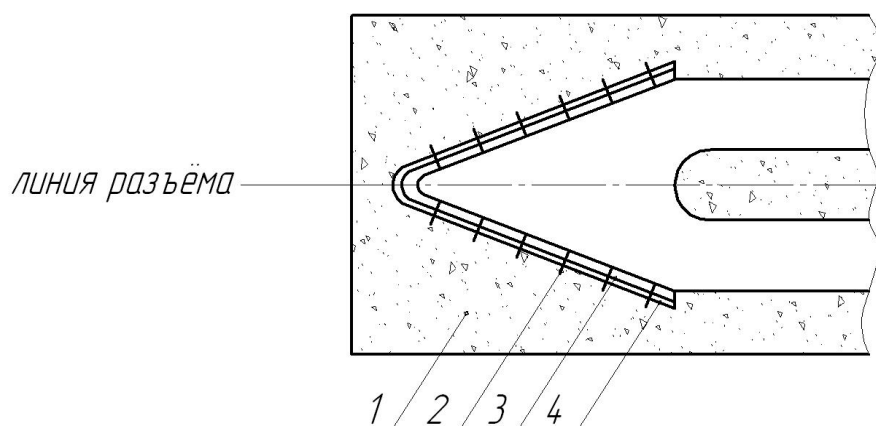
Литейная форма для изготовления отливок с углеродным покрытием из ткани
